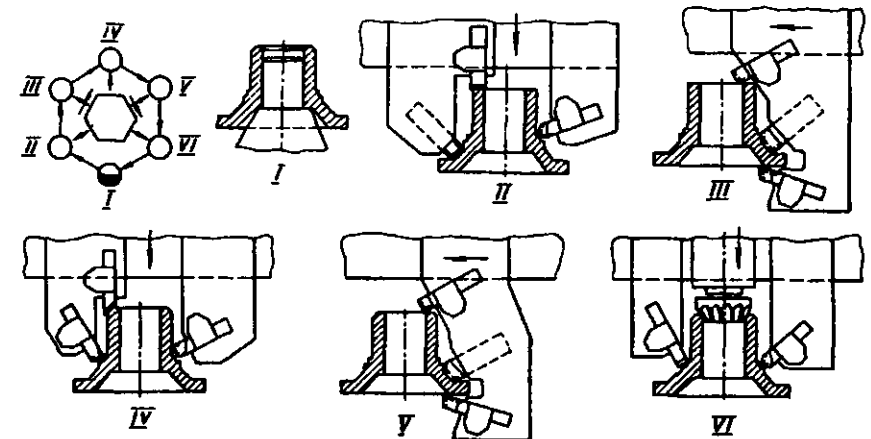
Наладка шестишпиндельного полуавтомата для одноцикловой обработки фланца
